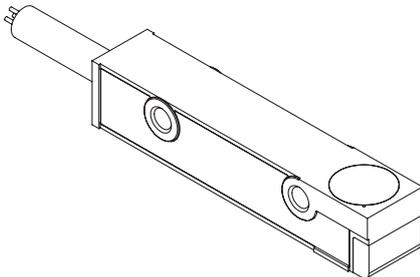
Endschalter für Linearachsen HM/HT/HC
